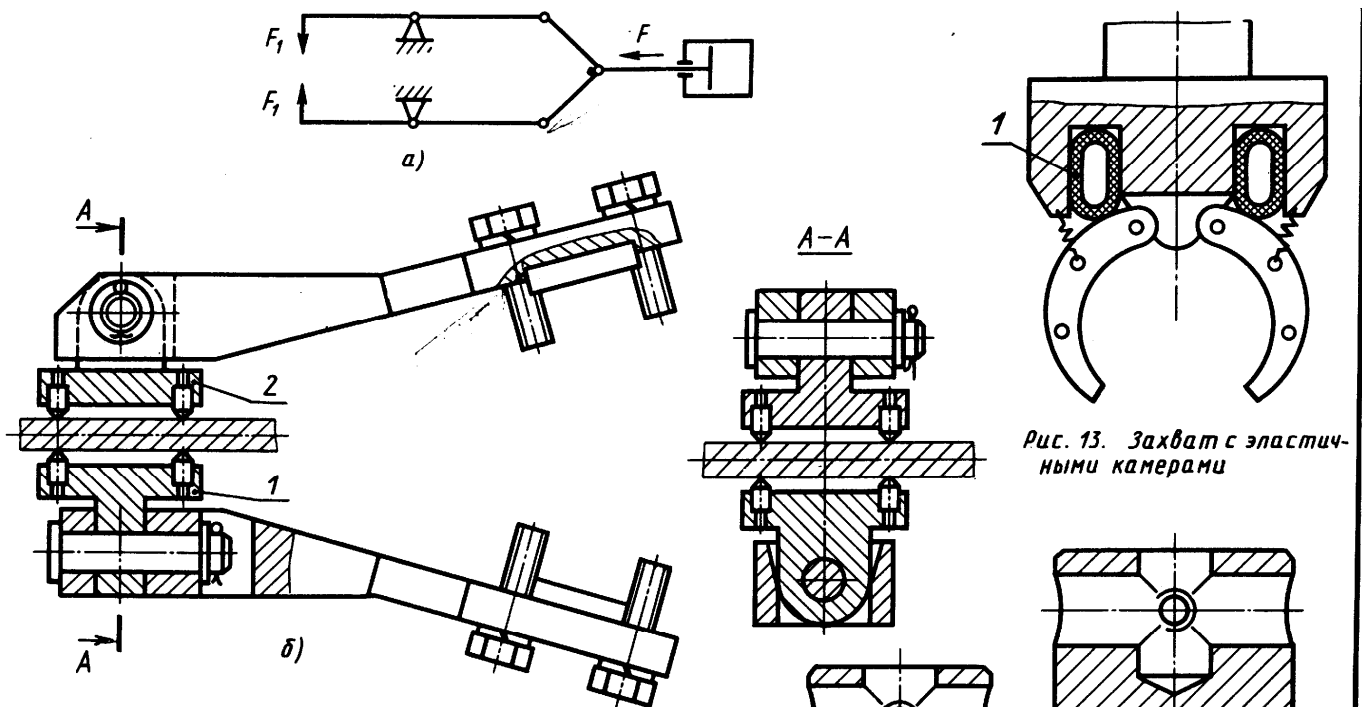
Самоустанавливающийся рычажный захват: а - схема; б - конструкция
